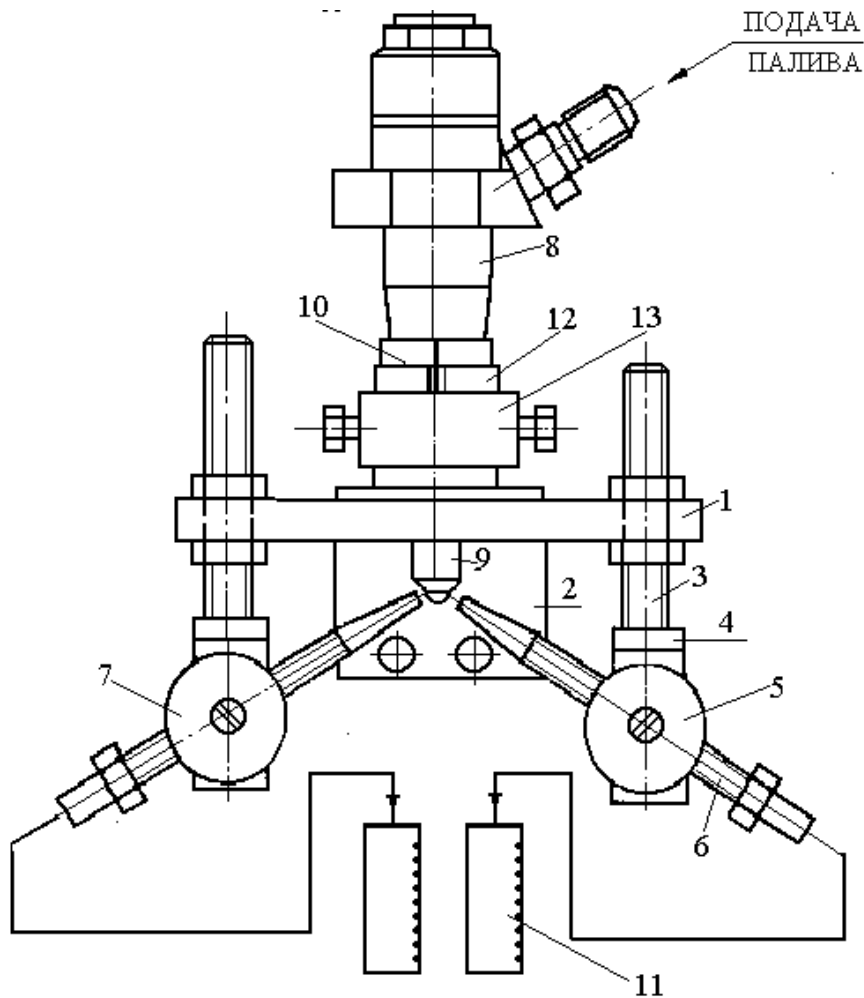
Пристрій для тестування розпилювачів: 1 – корпус; 2 – кронштейн; 3 – стійка збірника; 4 – кутник; 5 – шарнір; 6 – уловлювач; 7 – фіксатор; 8 – форсунка; 9 – розпилювач; 10 – мітки; 11 – колби; 12 – маточина; 13 – хомут.
